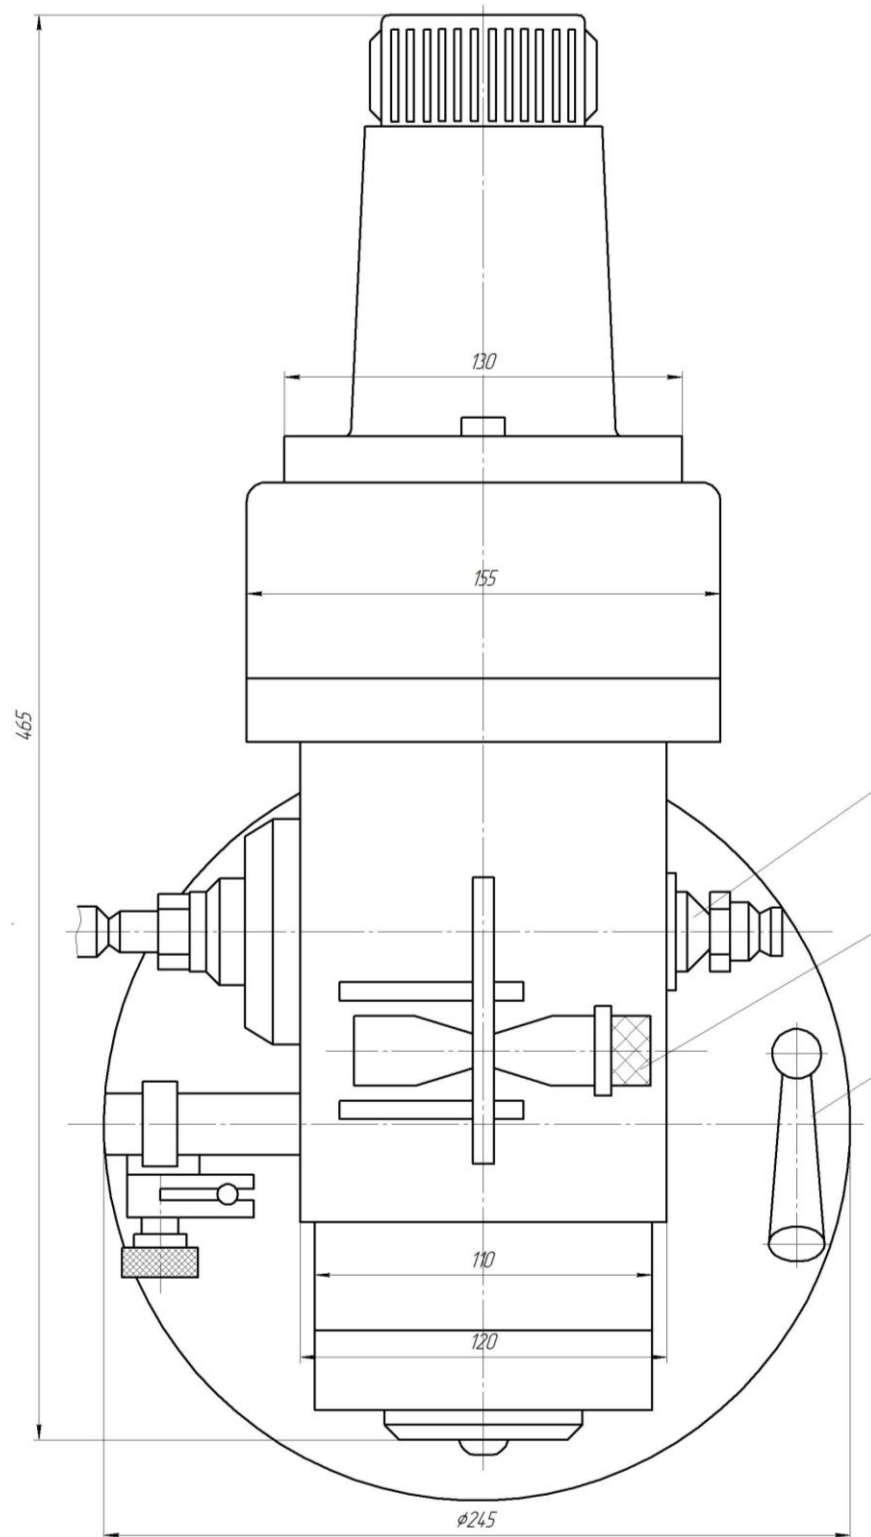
Вертикальна шпindelь наголовка базової моделі верстата.
